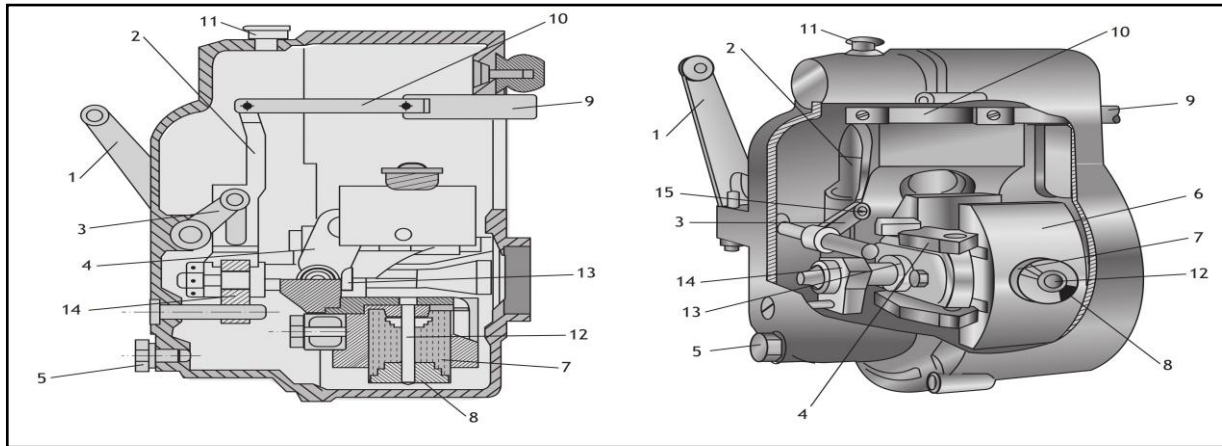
Regulador mecánico centrífugo de máxima y mínima. (Sánchez, *Sistemas Auxiliares del Motor*, 2103)
